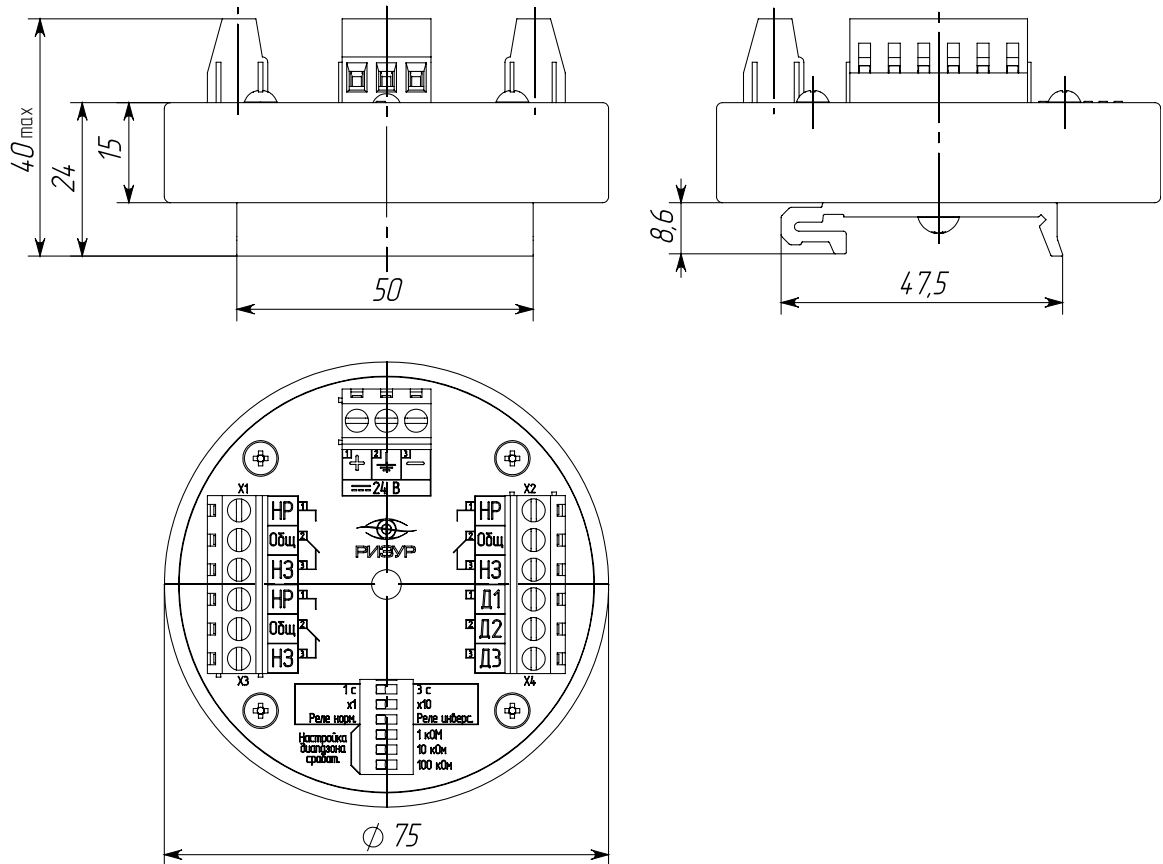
Габаритные размеры корпуса сигнализатора
